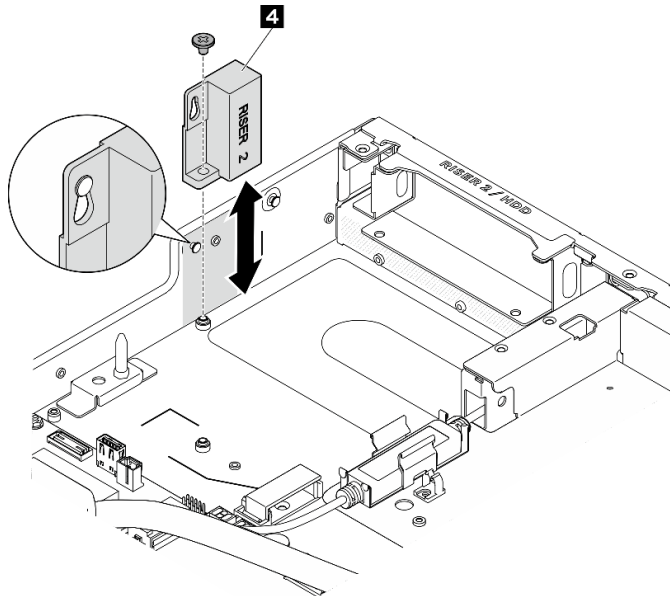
Installieren der DPU-Luftführung am Gehäuse
